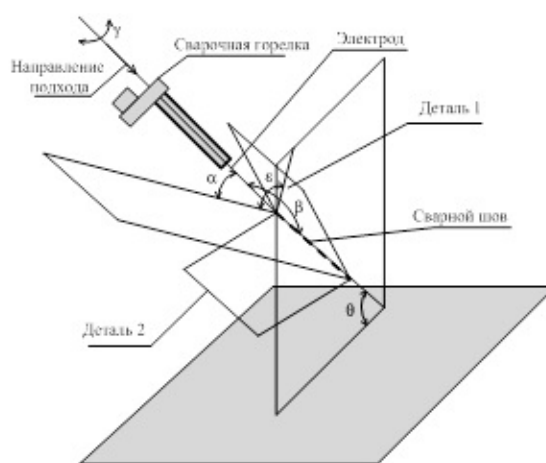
Ориентация горелки дуговой сварки и сварного шва
